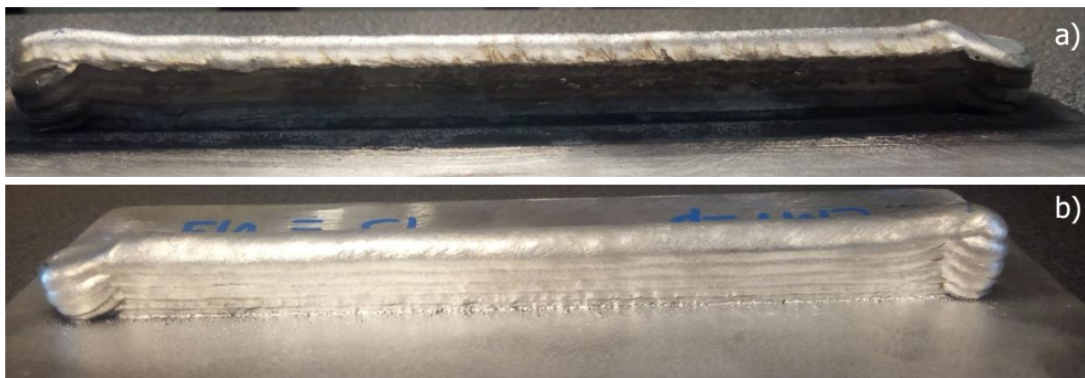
Dépôts multicouches (10 couches) : a) Couches non brossées, b) Couches brossées
